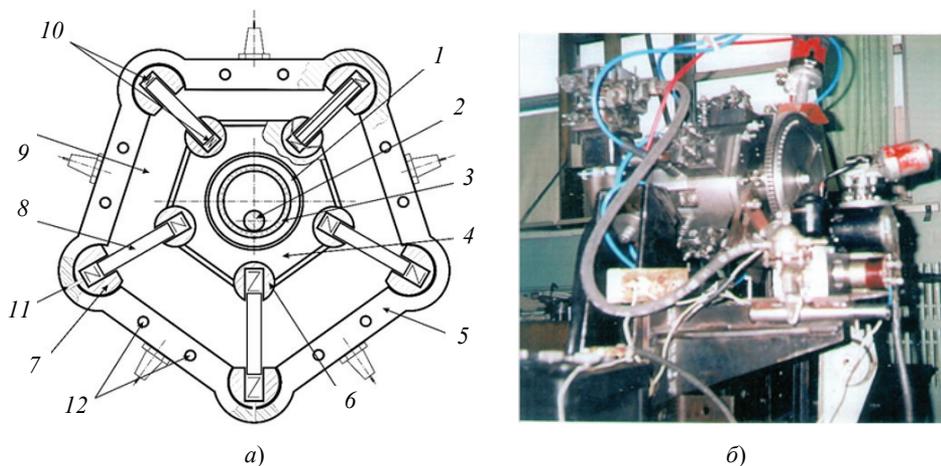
Конструктивная схема (а) и внешний вид (б) двигателя Воробьева:
